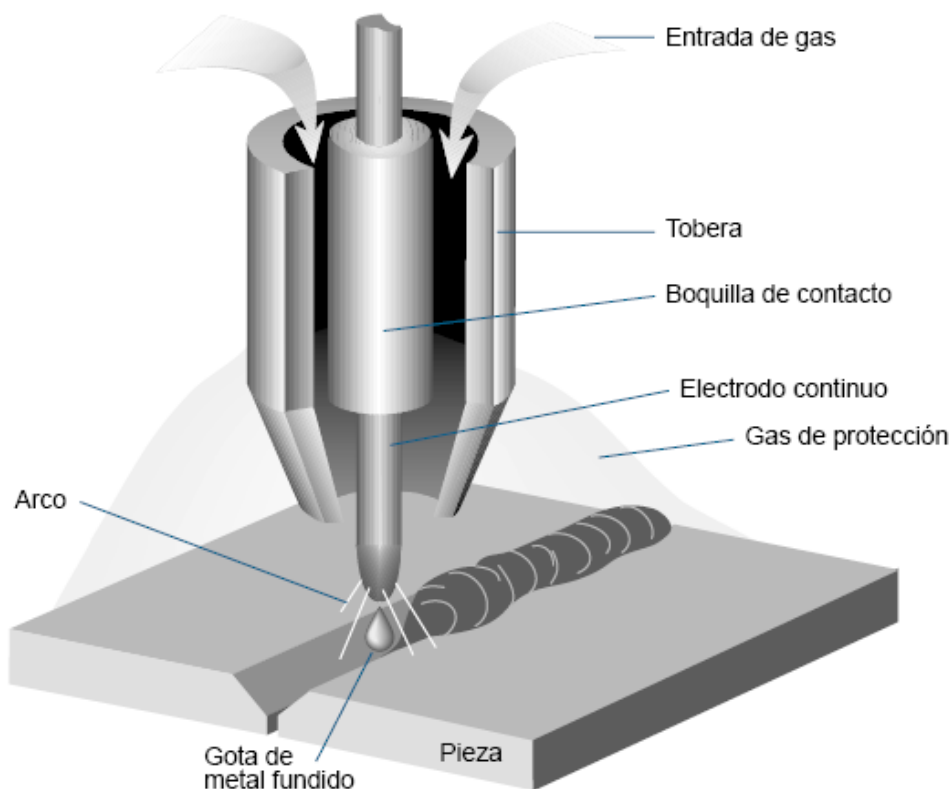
PROCESO DE SOLDADURA POR ARCO CON ALAMBRE CONTINUO PROTEGIDO CON GAS.
